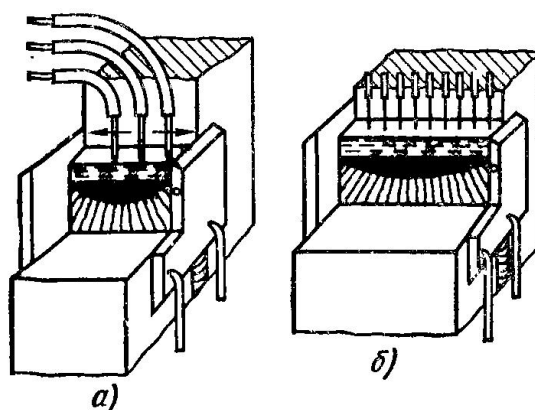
Схемы процесса многоэлектродной электрошлаковой сварки:
